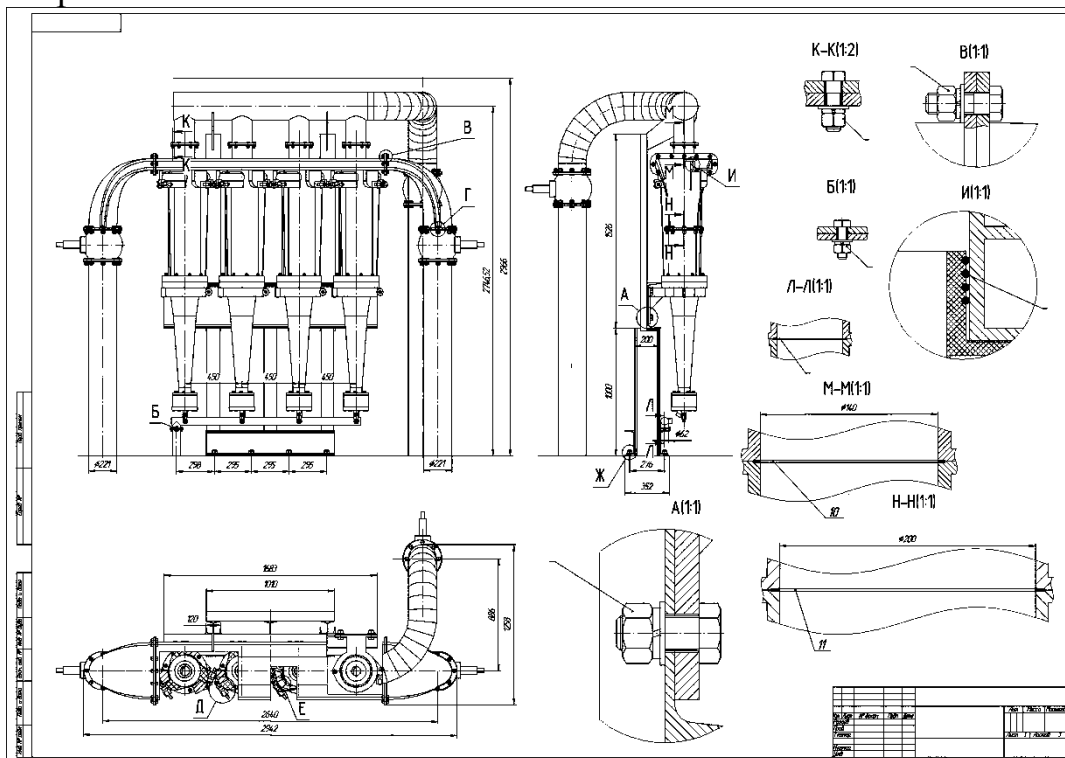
Сборочный чертеж батареи вихревых очистителей
